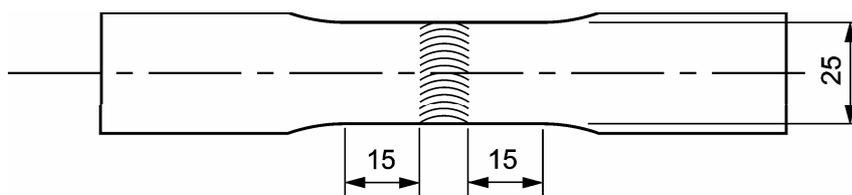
Probekörper für den Zugversuch, senkrecht zur Schweißnaht
